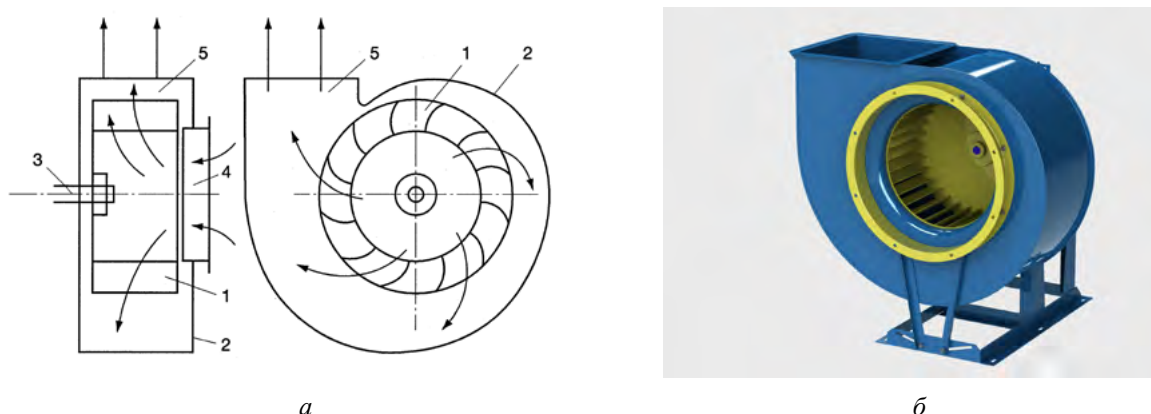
Схема (а) и вид (б) радиального вентилятора: 1 — рабочее колесо с лопатками; 2 — спиральный кожух; 3 — вал; 4 — воздухоприемный коллектор; 5 — выходной коллектор
